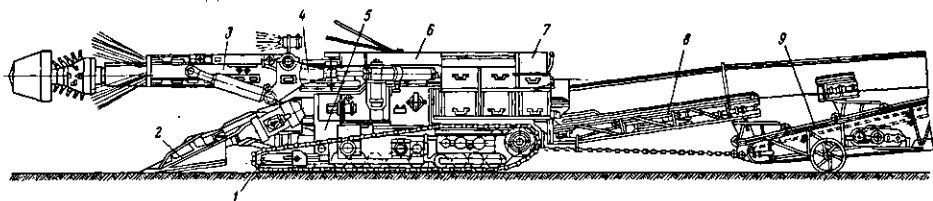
Комбайн 4ПП2: 1 – механизм передвижения; 2 – погрузочное устройство; 3 – исполнительный орган; опорно-вращательный механизм; 5 – корпус комбайна; 6 – система пылеподавления; 7 – электро- и гидросистемы; 8 – мостовой перегружатель; 9 – прицепной перегружатель
